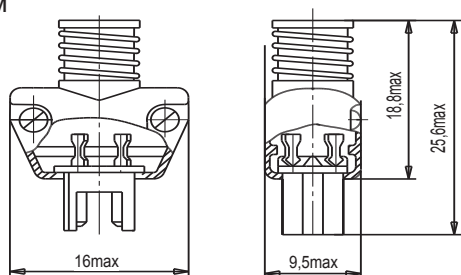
Вилка РШ2Н-1-6 с угловым металлическим кожухом
